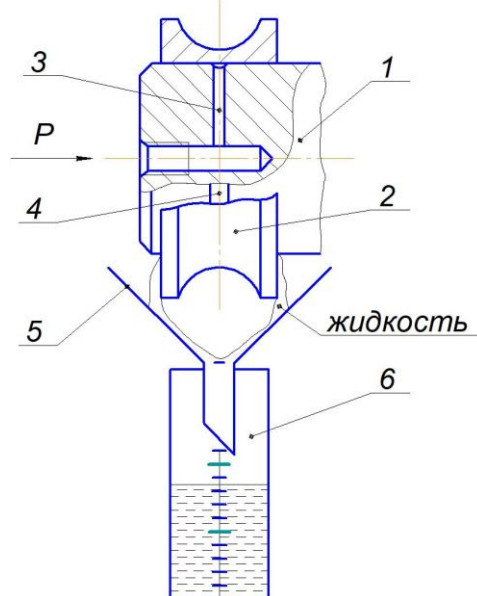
Схема применения способа безразборной оценки неподвижного соединения с натягом: 1 – вал; 2 – кольцо подшипника качения; 3 – радиальный канал; 4 – распределительная канавка; 5 – воронка; 6 – мерный стакан; P – давление рабочей жидкости.
